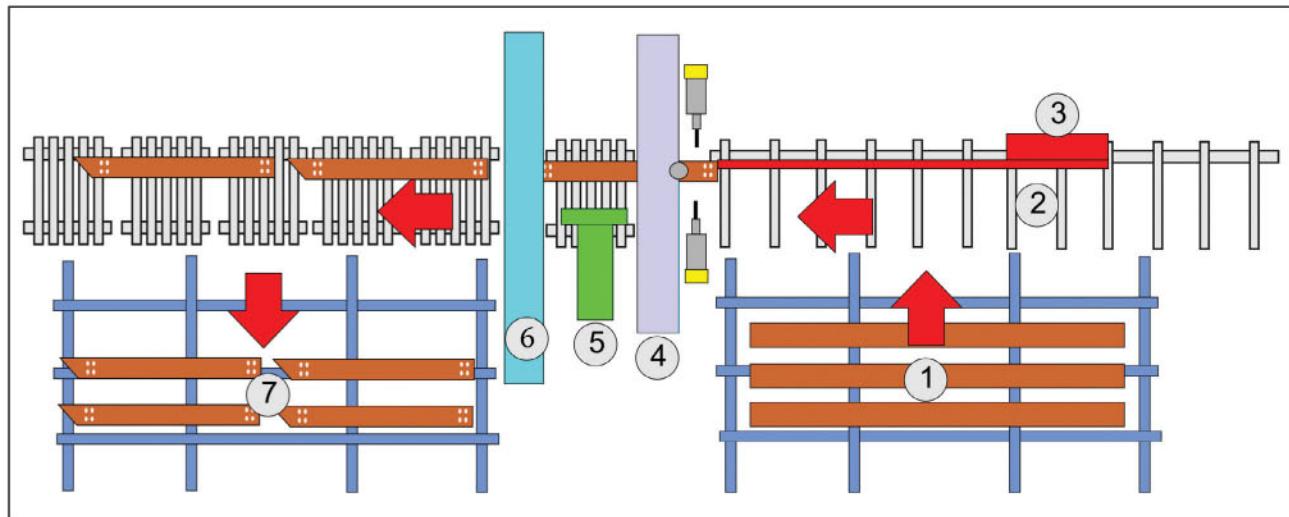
Линия сверловки, маркировки и мерной порезки профильного проката: 1 — загрузочный конвейер; 2 — транспортная система; 3 — подающее устройство; 4 — установка для сверления в трех плоскостях; 5 — установка для маркировки; 6 — установка для мерной порезки; 7 — принимающий конвейер
